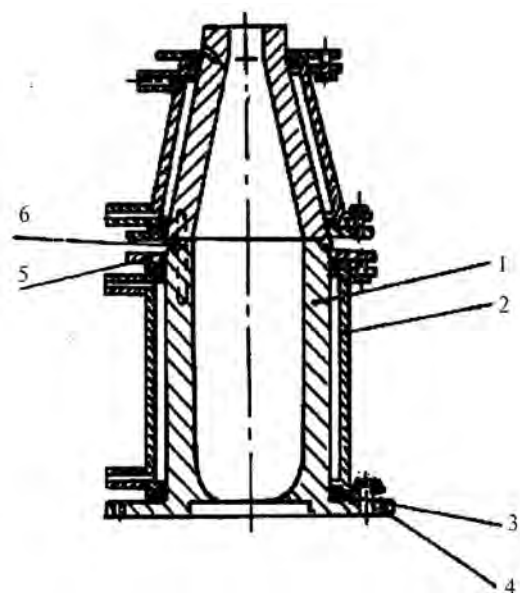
Конструкция водоохлаждаемой металлической формы: 1 - рабочая стенка формы; 2 - кожух водяного охлаждения, 3 - резиновый уплотнитель; 4 - фланец; 5 - скользящий фланец, 6 - линия разъема формы
